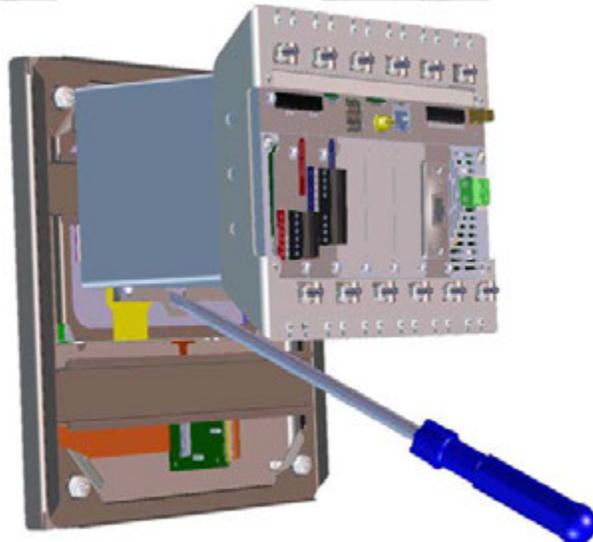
Extracción del conjunto del controlador del carril DIN
